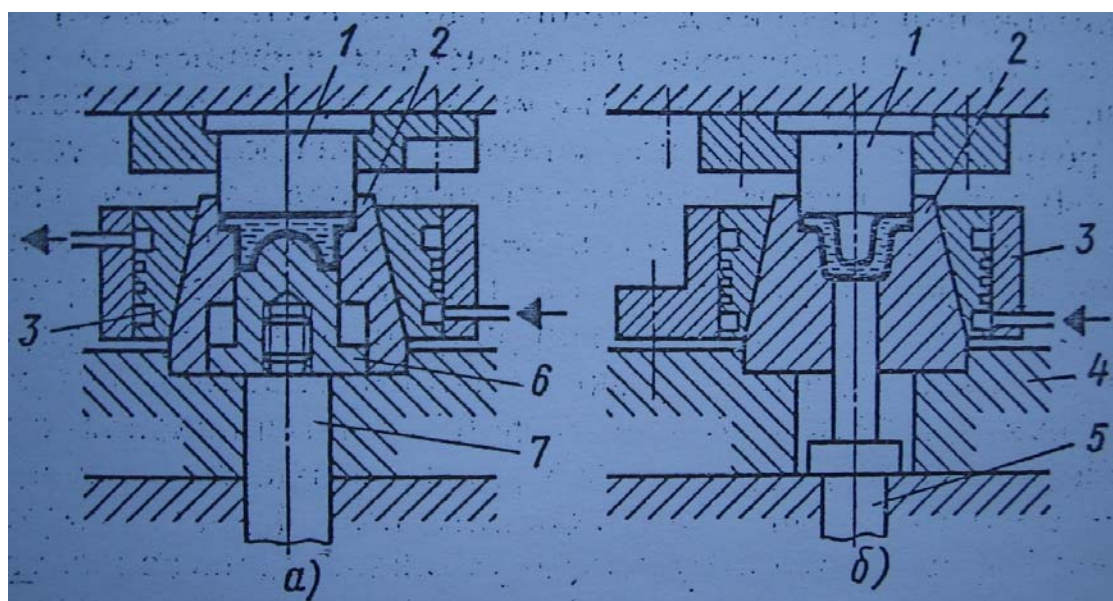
Формоблоки для кристаллизации под давлением (а) и штамповки из расплава (б).
